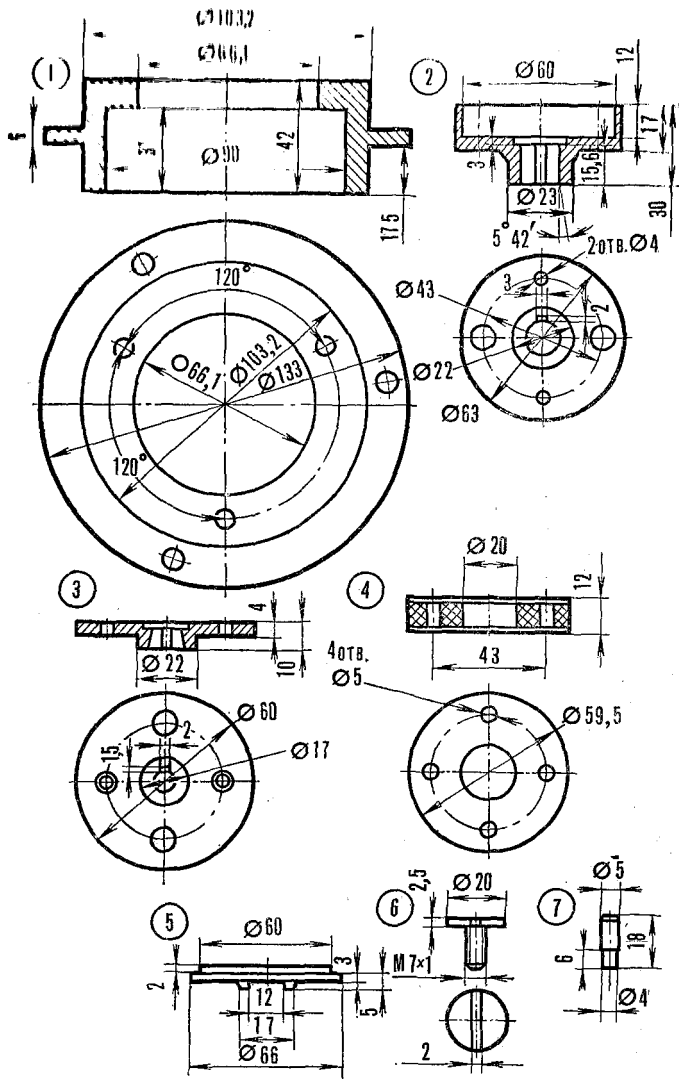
Детали для установки магнето: 1 — шайба-подставка (Д-16Т, В-95); 2 — фланец коленчатого вала (сталь Ст. 3); 3 — фланец вала магнето (сталь Ст. 3); 4 — соединительная муфта (резина); 5 — крышка (Д-16Т); 6 — болт (сталь Ст. 3); 7 — штырь (сталь Ст. 3). Конусные отверстия в дет. 2 и 3 подгоняются по валам
